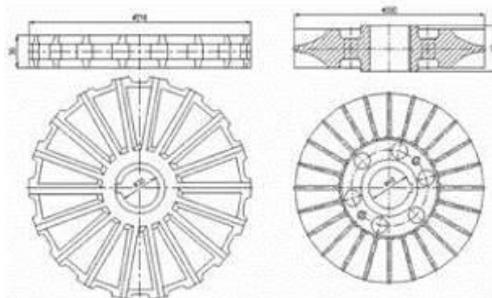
Общий вид колеса вихревого насоса СВН-80
